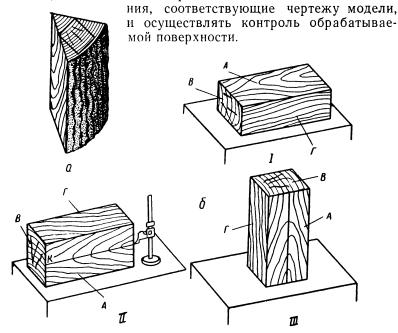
Заготовка геометрической формы для моделирования колодок по чертежу:
